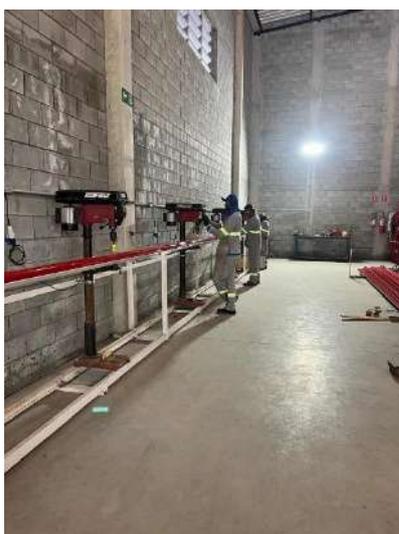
Bancada para furação de ramais (Fonte: Autora)
